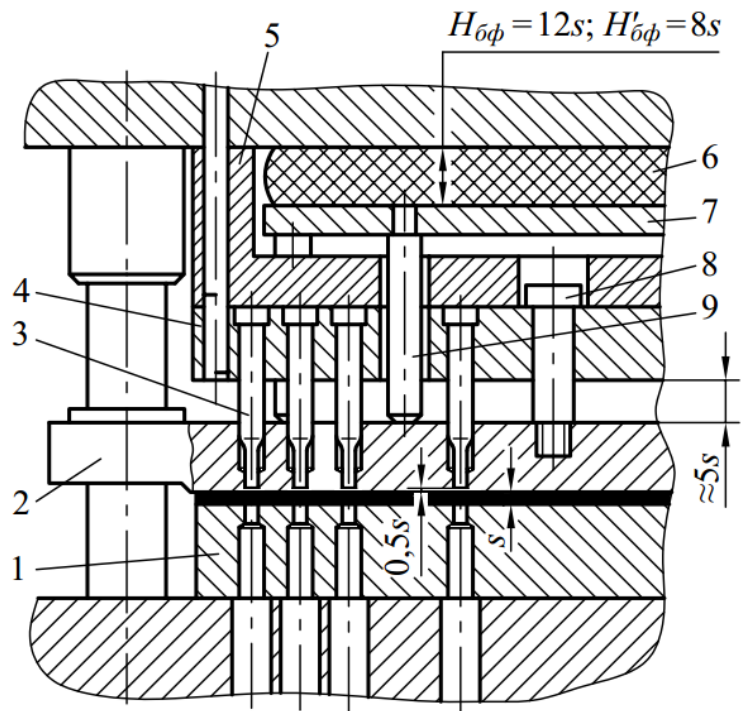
Схема штампа для пробивання отворів: 1 – матриця; 2 – притискувач;
